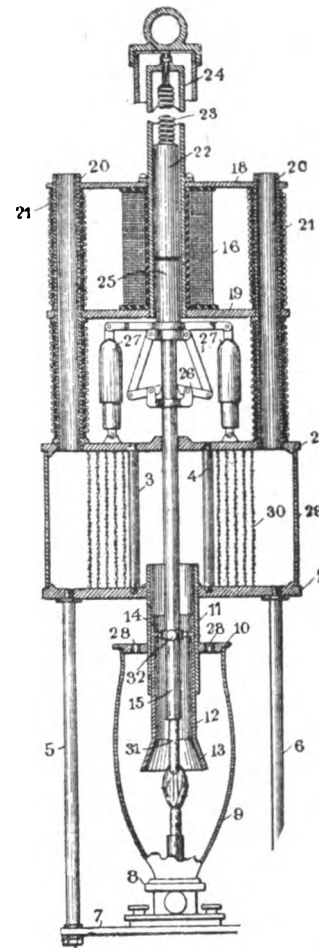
Lampada della "General Electric Company" a Schenectady.
